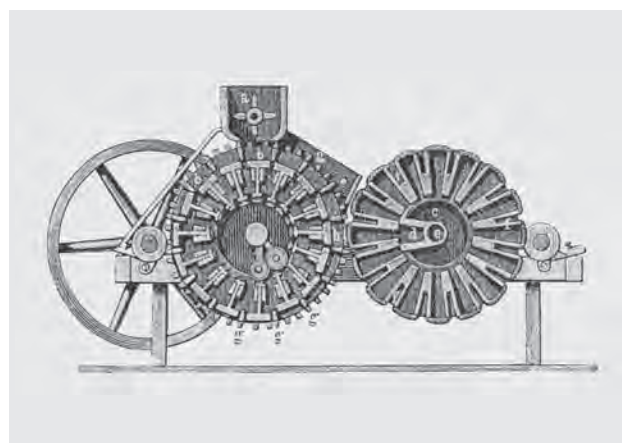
Ziegelmaschine mit rotierendem Formenrad und inne-
